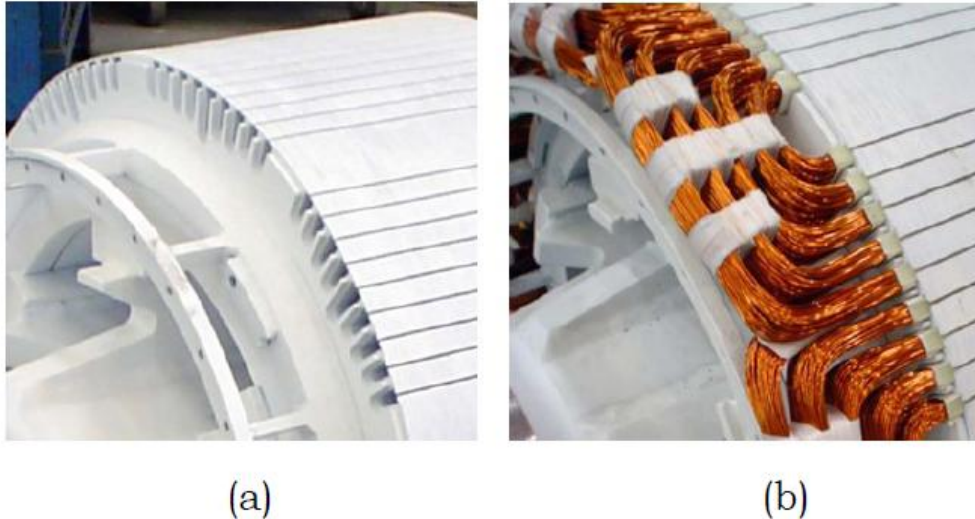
Rotor de la MADAB: (a) Rotor sans conducteur; (b) Rotor Bobiné [18].
